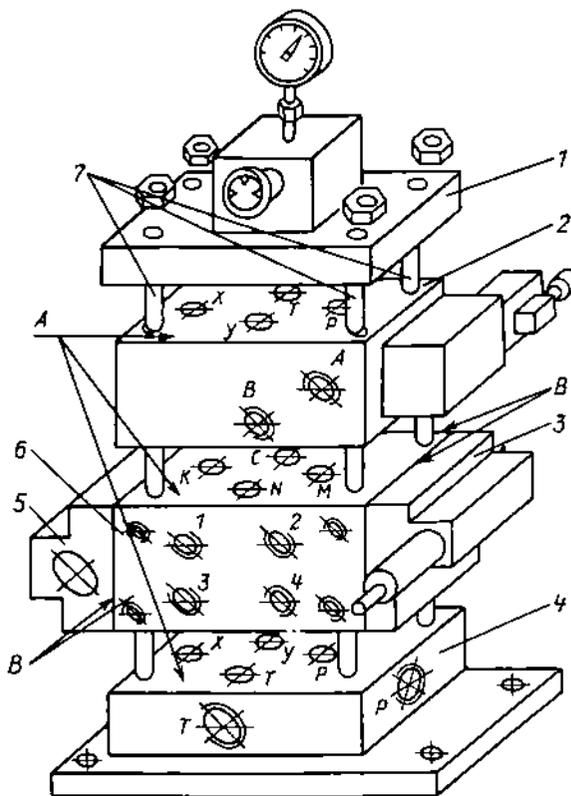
Гидроблок управления: 1 — блок замыкающий переключателя манометра; 2 — блок распределителя; 3 — блок присоединительный; 4 — блок замыкающий подвода; 5 — блок присоединительный; 6 — соединительно-монтажный модуль; 7 — стяжные шпильки
